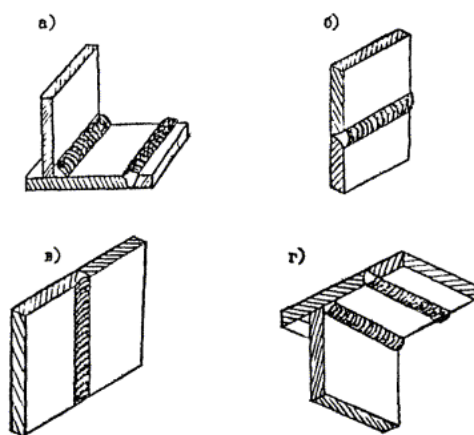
Способы сварки: а)нижний, б) горизонтальный, в) вертикальный, г) потолочный
